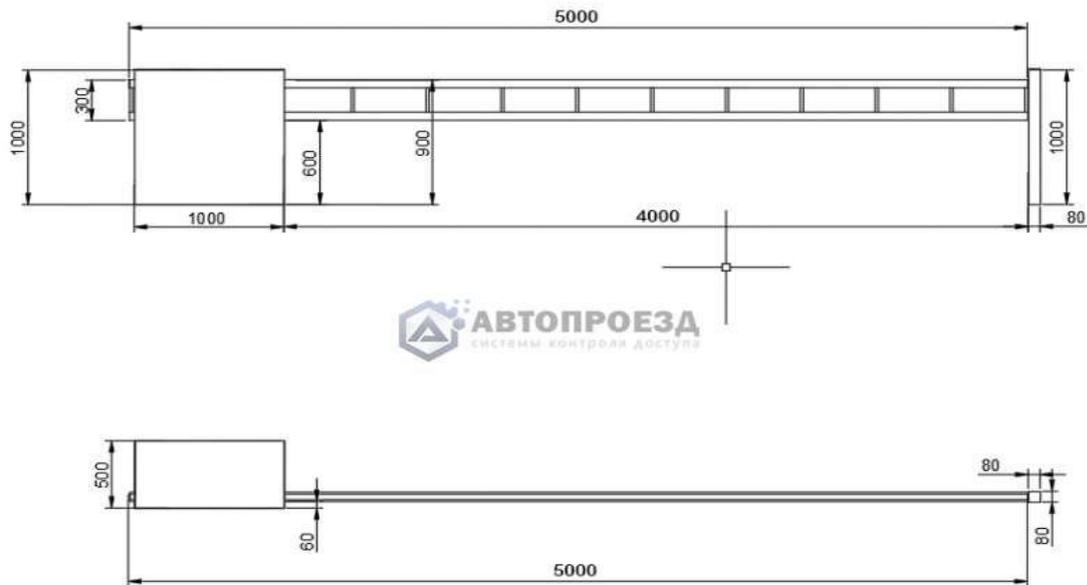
Чертеж размеров шлагбаума № 2
